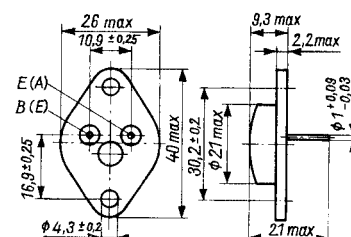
Gehäuseabmaße und Anschlußbelegung der CSSR-Typen (TO 3)
